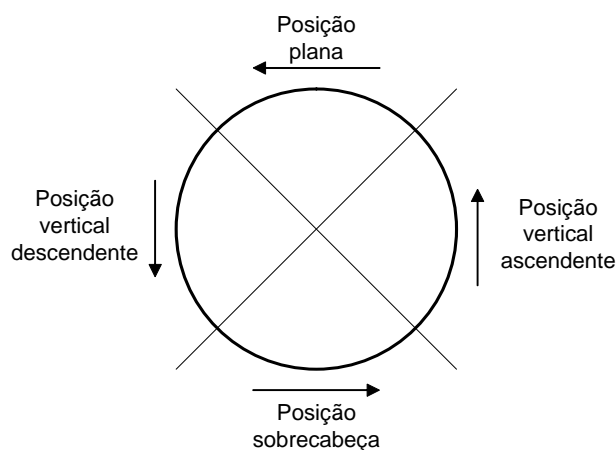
Posições de soldagem no tubo durante a soldagem orbital.
